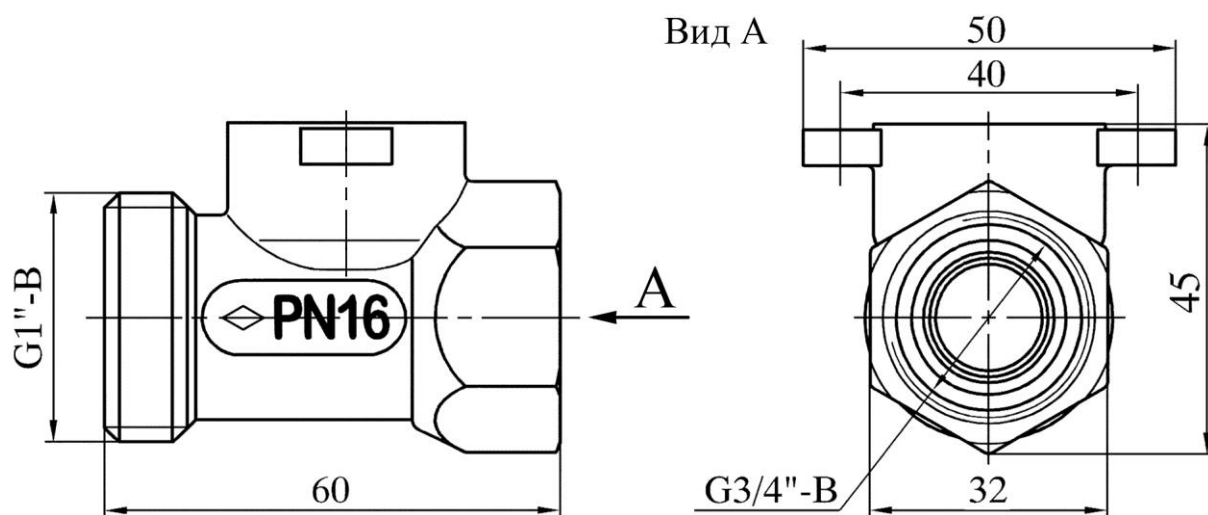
Корпус термоклапана (латунный с резьбовым присоединением)
